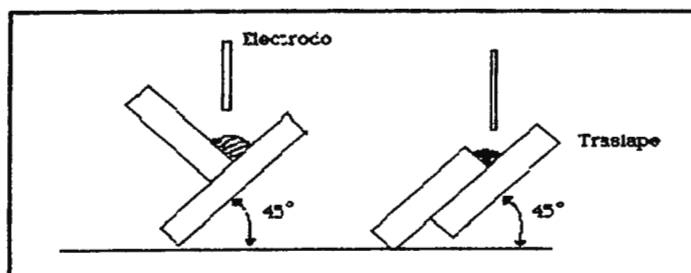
Soldadura de filete hacia abajo
